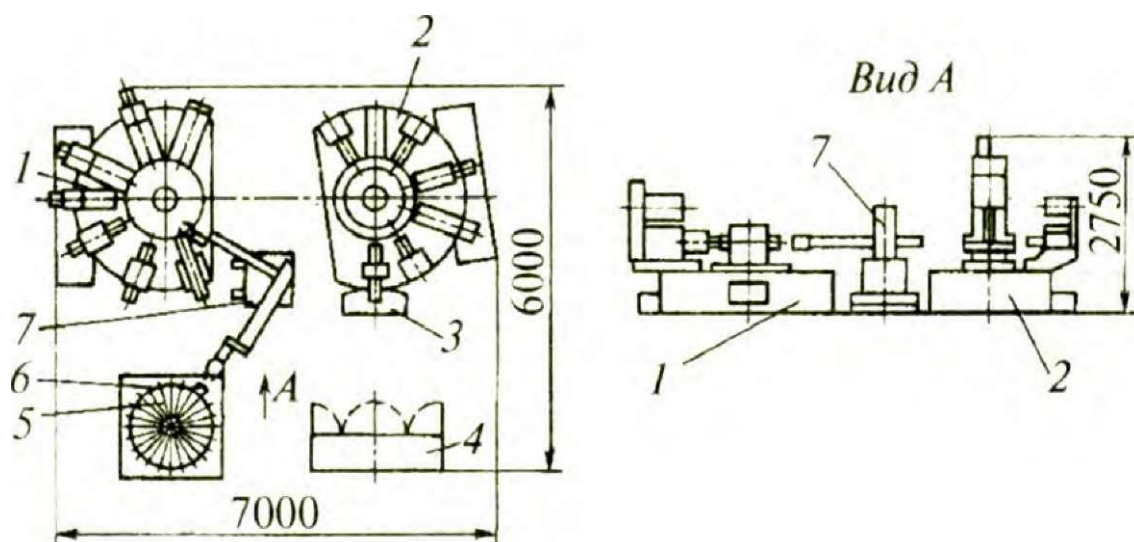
Роботизированный технологический комплекс для обработки малогабаритных корпусных деталей
